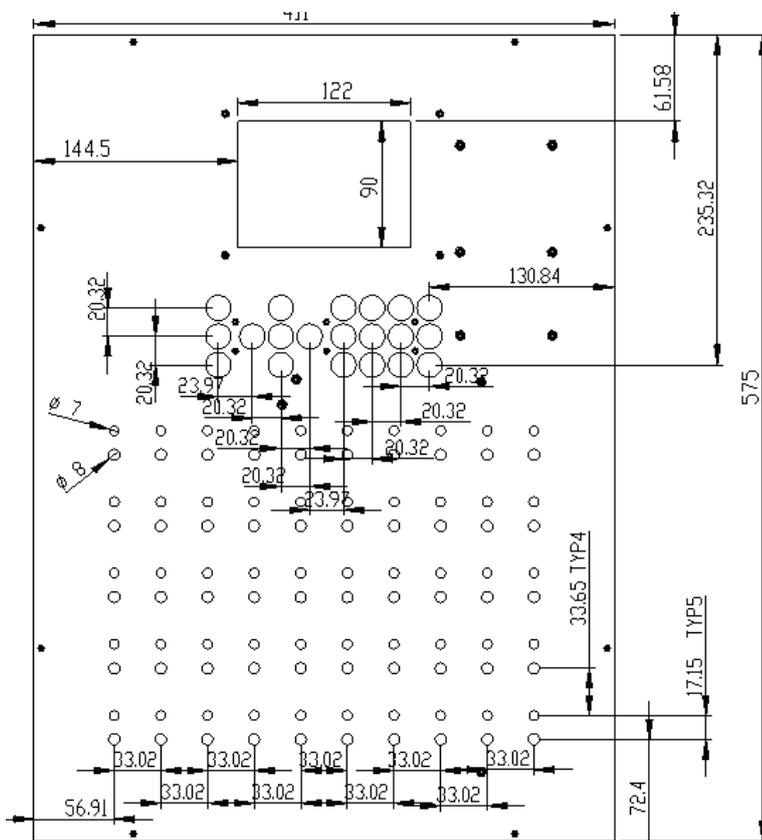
Dimensiones del Panel Frontal del Platinum Pro 50
